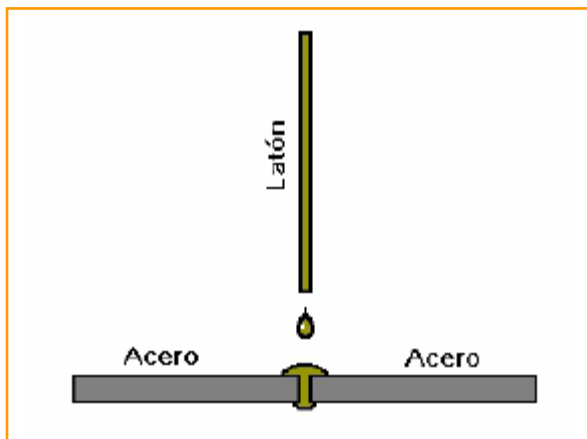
Ejemplo de soldadura heterogénea.
